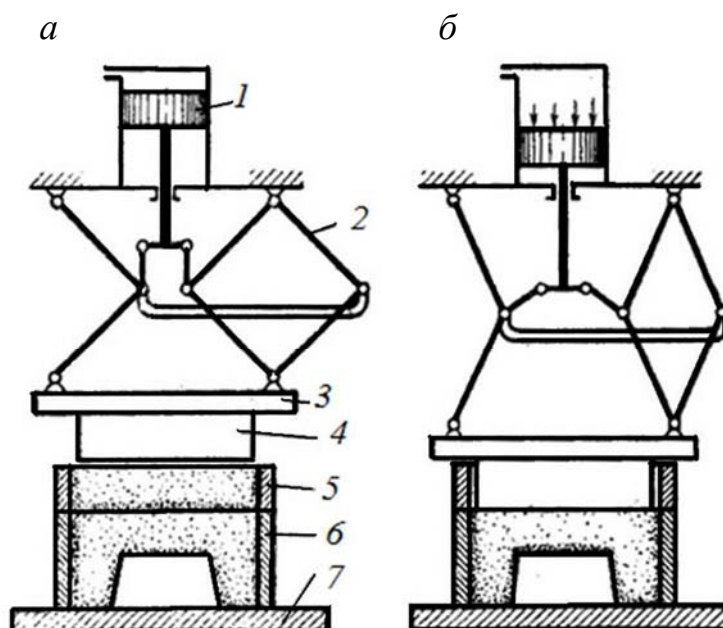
Схема рычажного механизма прессовой формовочной машины:
